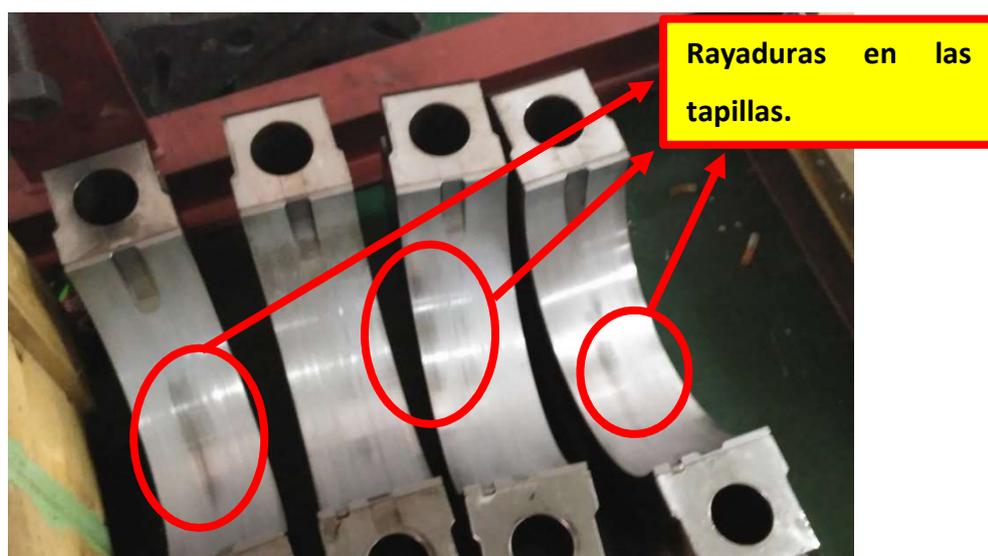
Detalle tapillas dañadas. Fuente: Trabajo de campo.
